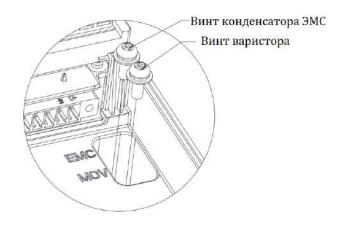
Соединительные винты конденсатора ЭМС и варистора
